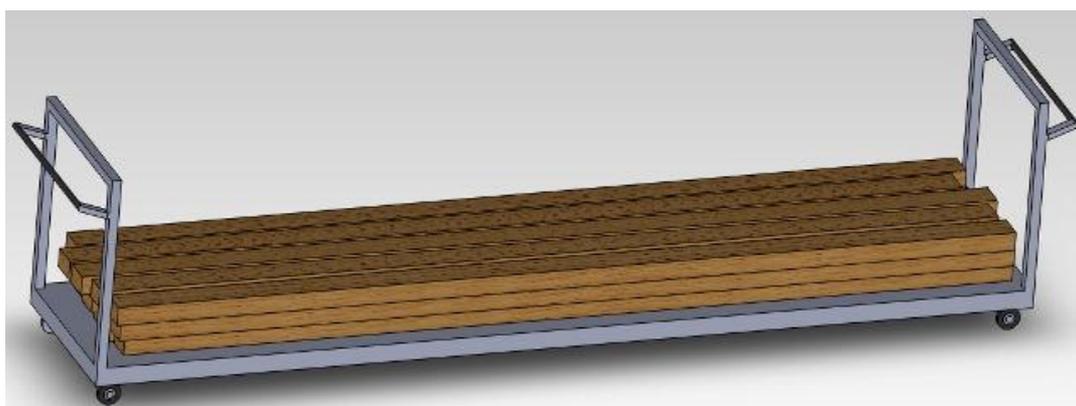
Carrinho para transporte de vigas para uso interno no armazém
